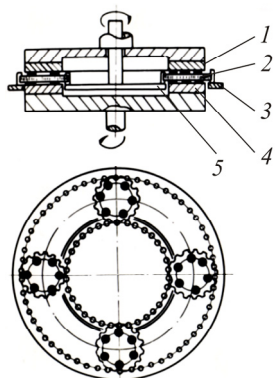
Схема станка Peter Wolters с планетарными сепараторами
